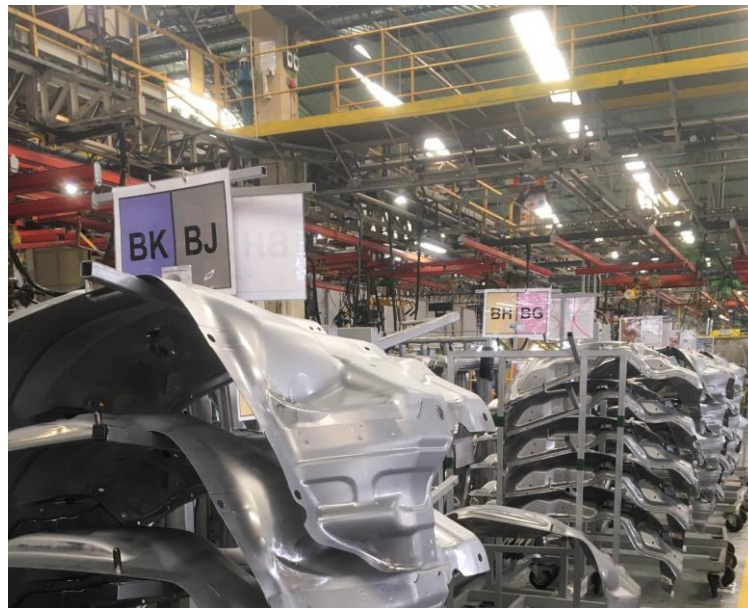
Exemplo da disposição do material nos supermercados da Soldadura (Fonte: O Autor)
